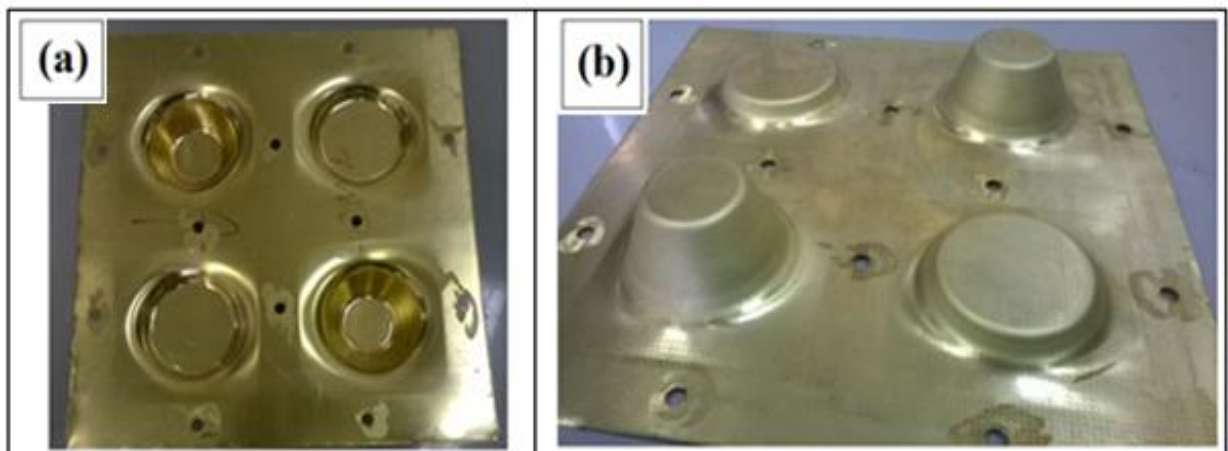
Chapa estampada. (a) Parte superior; (b) Parte inferior.
